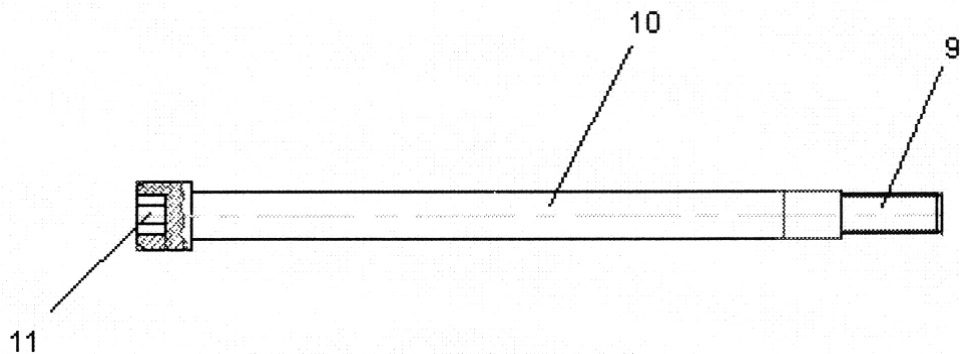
Фиксатор и его типовые размеры для крепления противовесов на вал компрессора фреона
